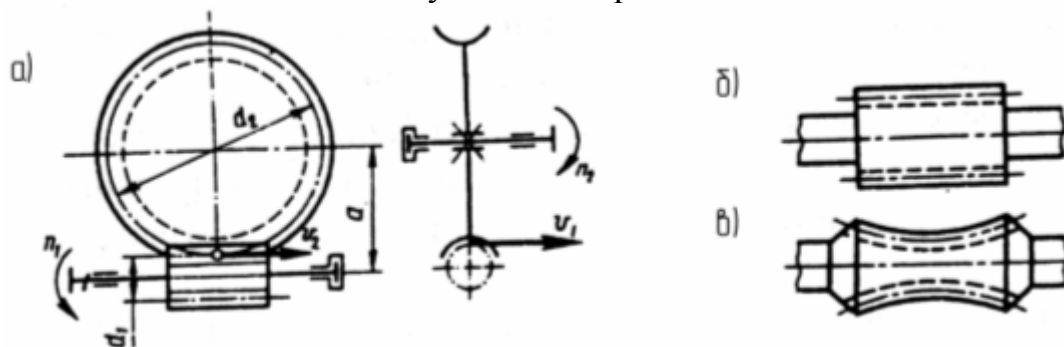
Схема черв'ячної передачі ліфтового редуктора:
